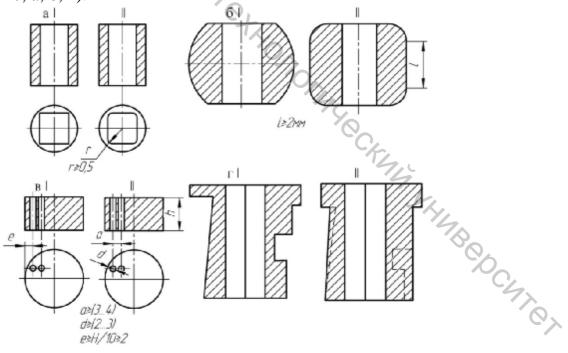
Нерациональные (I) и рациональные (II) конструкции порошковых деталей: а – с прямоугольными отверстиями; б – с плоскими площадками; в – с эксцентричными отверстиями; г – с прямоугольными пазами
